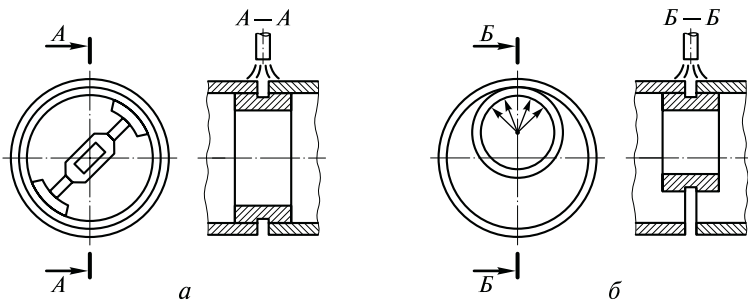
Флюсомедные подкладки для сварки кольцевых швов:
